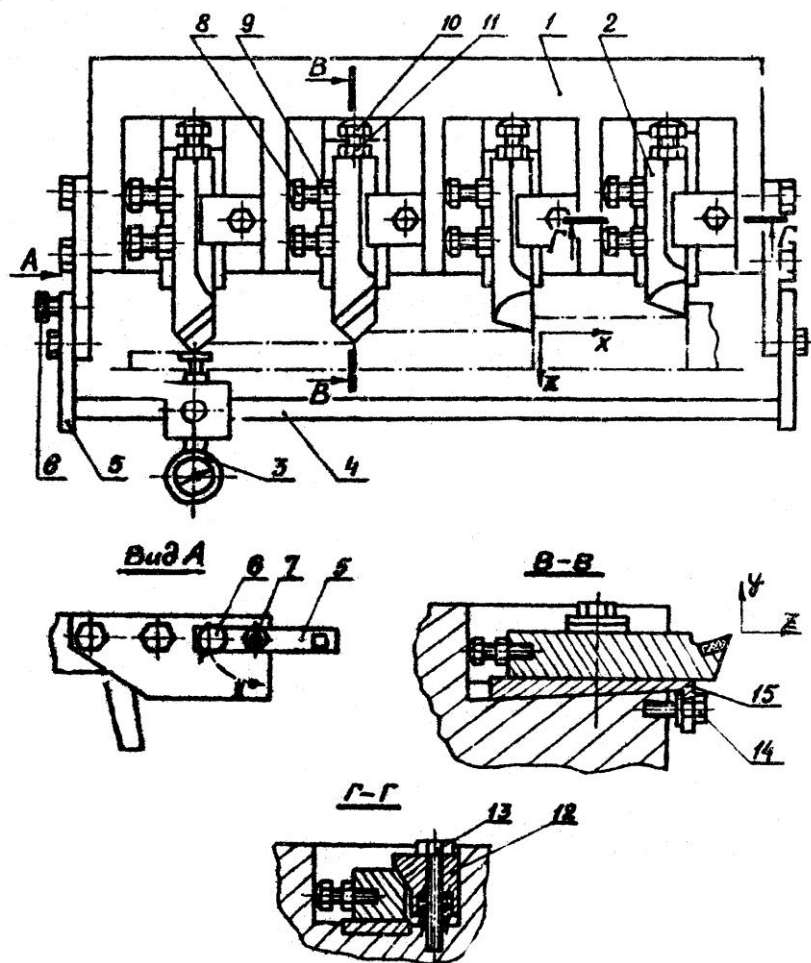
Блок резцов: 1 – корпус; 2 – резец; 3 – индикатор; 4 – направляющая; 5 – планка; 6 – винт фиксации планки; 7 – ось планки; 8, 9 – установочные винт и контргайка (ось x); 10, 11 – установочные винт и контргайка (ось z); 12 – прижим; 13 – винт; 14 – винт; 15 – клин
